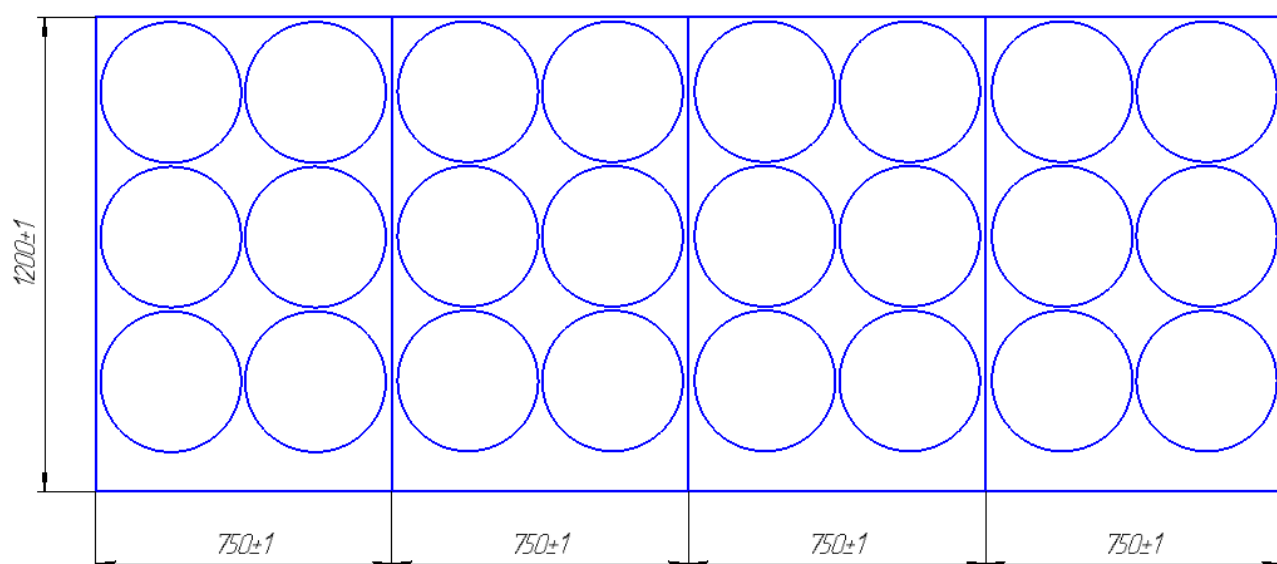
Схема резки заготовок для дисков колеса рабочего
